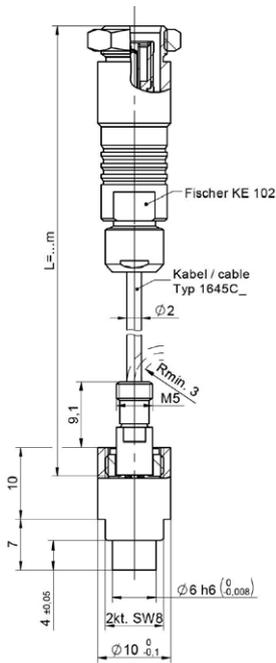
Drucksensor Typ 6172B mit Koaxial Kabel
